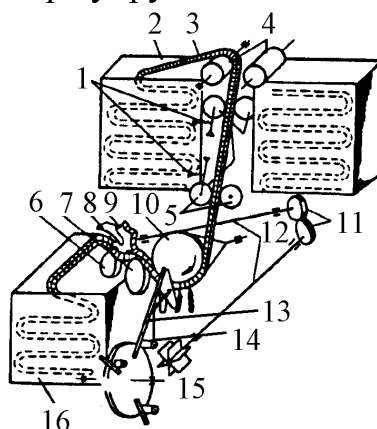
Схема лесопосадочного автомата ПЛА-1А: 1 – пружины; 2 – контейнер; 3 – кассетный сеянцедержатель; 4 – направляющий валик; 5 – ролик; 6, 7 – прижимные ролики; 8 – отсекатель; 9 – ведущая звездочка; 10 – ролик профильный; 11 – зубчатые колеса; 12 – вал привода; 13 – посадочный аппарат; 14 – упор; 15 – крыльчатка привода протяжки; 16 – контейнер с отработанной кассетой
